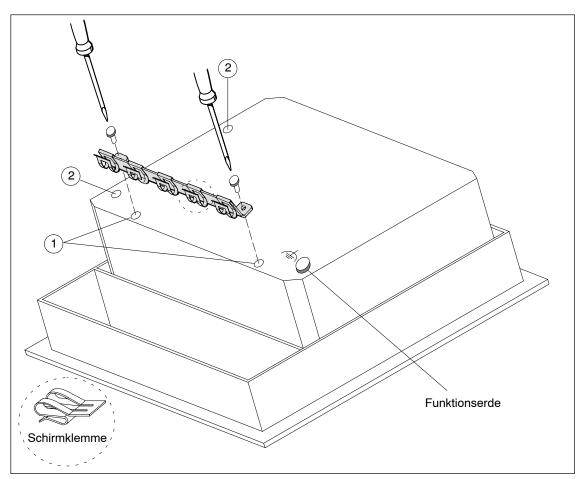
C7-635 mit Erdungsschiene, Schirmklemmen und Anschluss für Funktionserde
